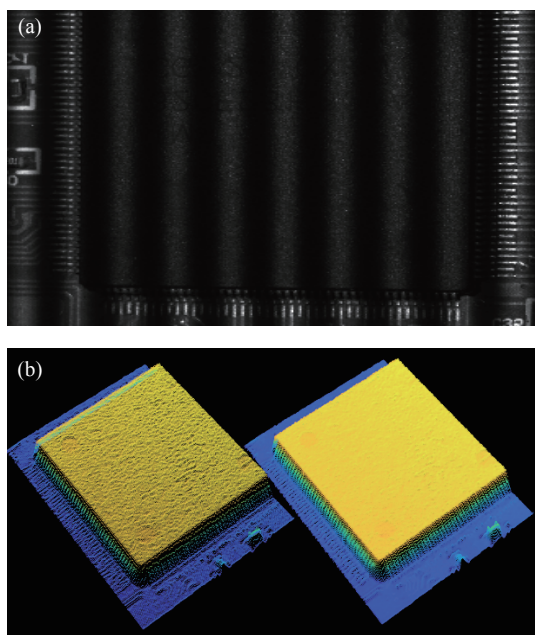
PCB 表面重建效果对比 (a) 原始条纹图像 (b) 点云超分辨率前后对比)
